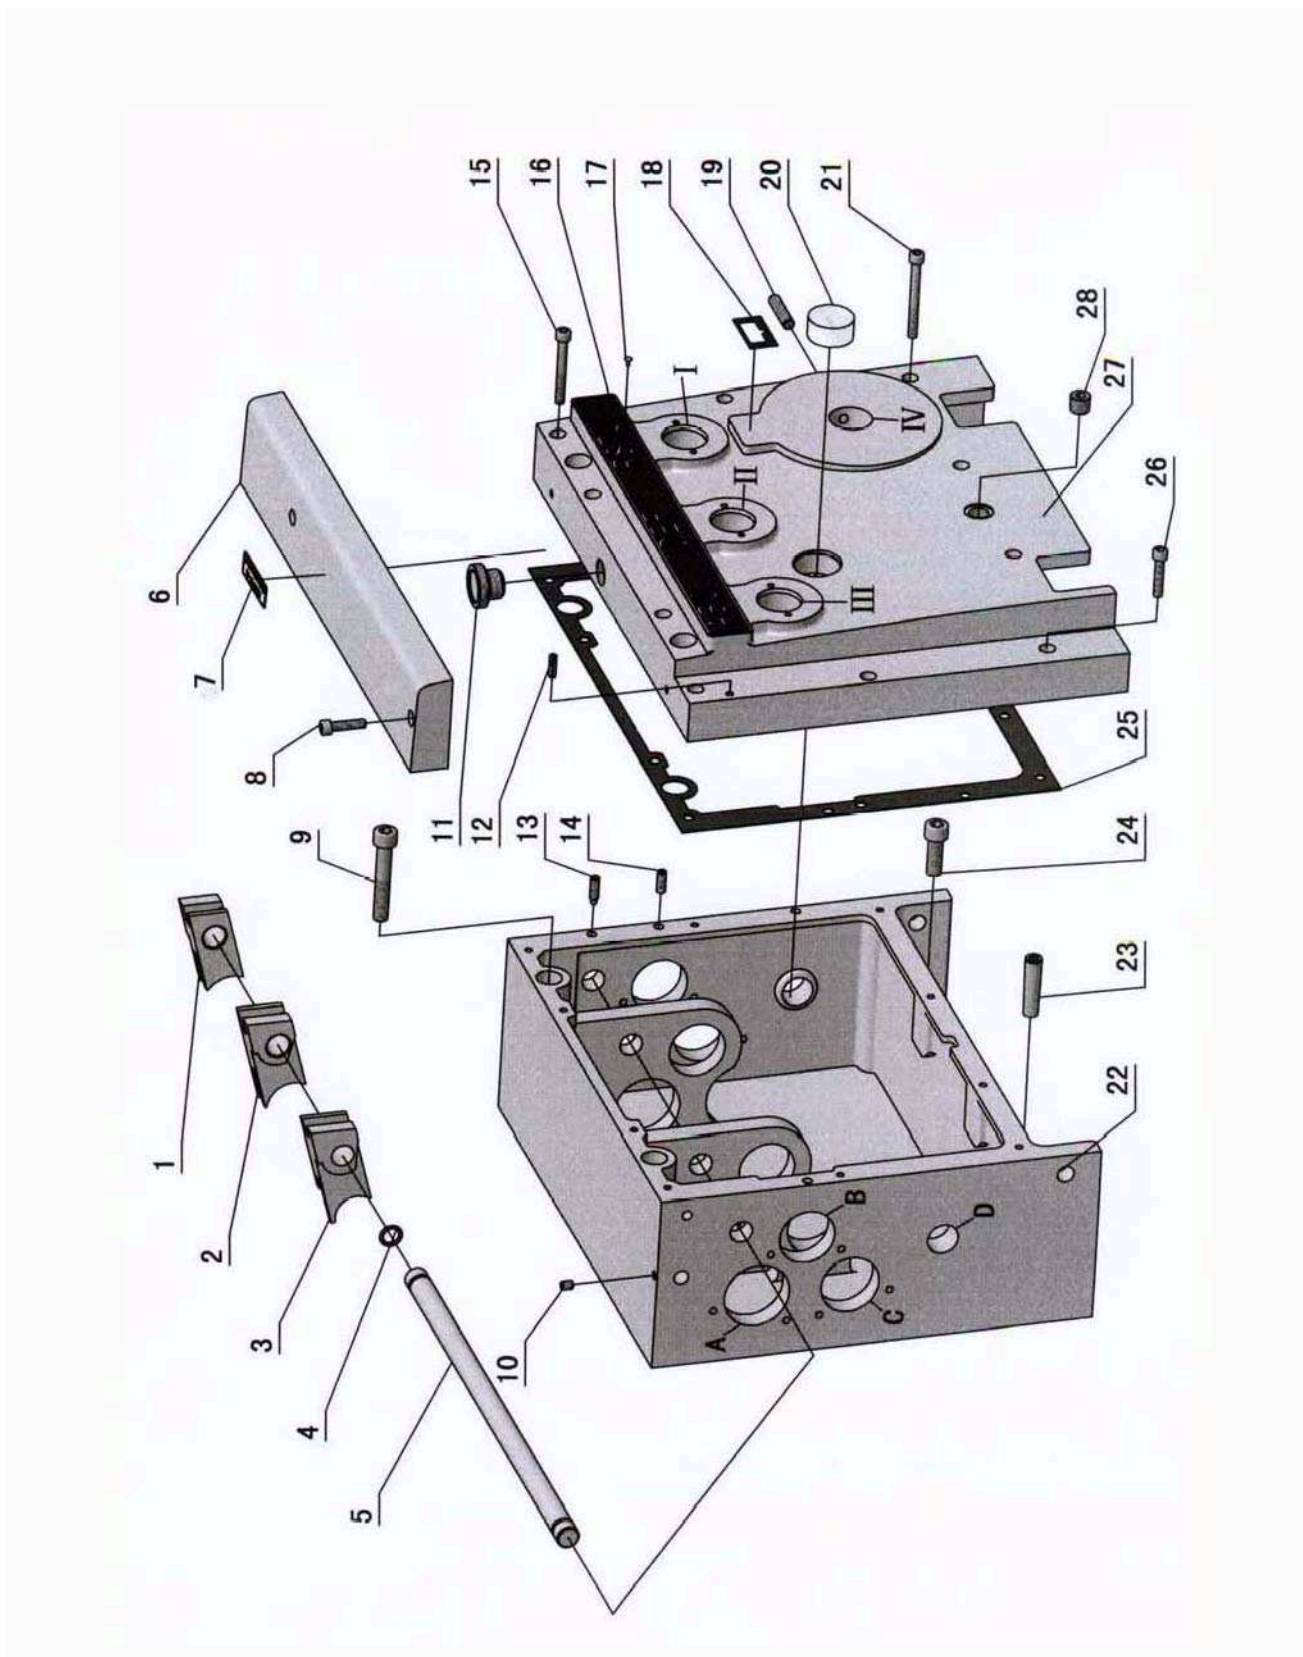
Vorschubgetriebe 1 von 4 - Headstock feed gear 1 of 4
